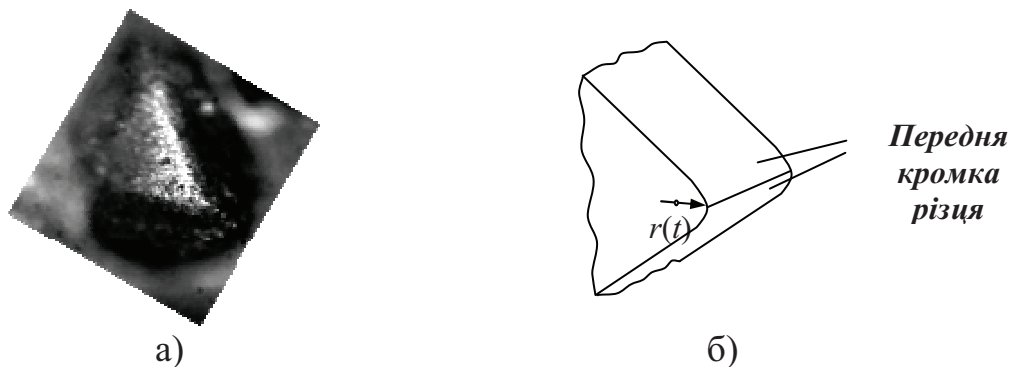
Робоча поверхня алмазного індентора: а) – фото; б) – схема
